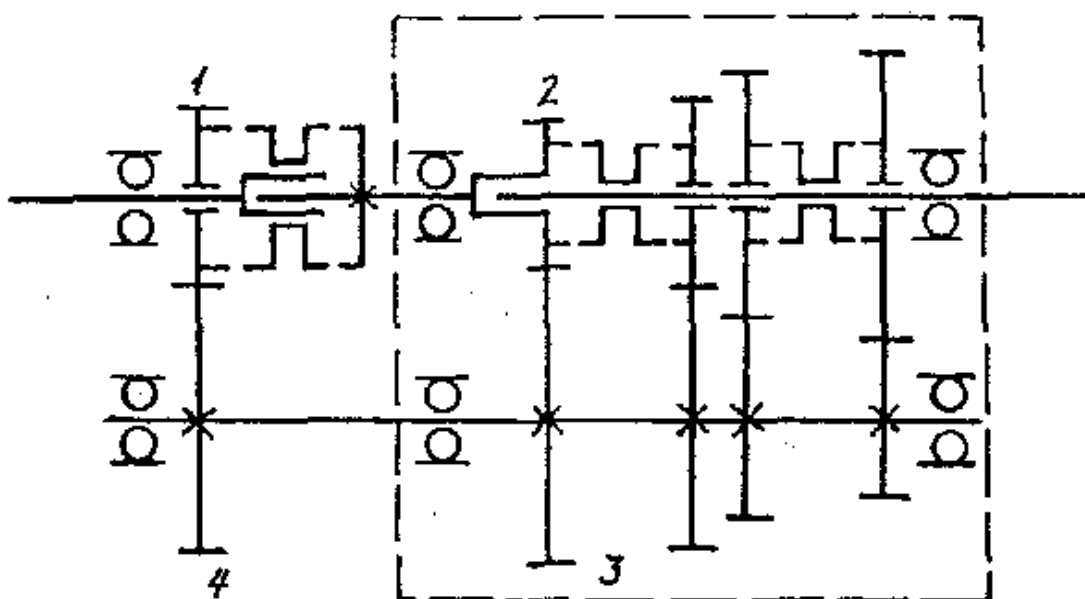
Кинематическая схема 4-х ступенчатой коробки передач с делителем и разрезным валом
